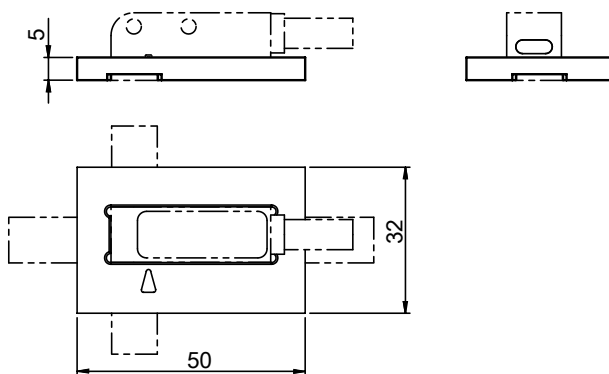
Guidage de capteur BAM TO-ML-019-SF2
